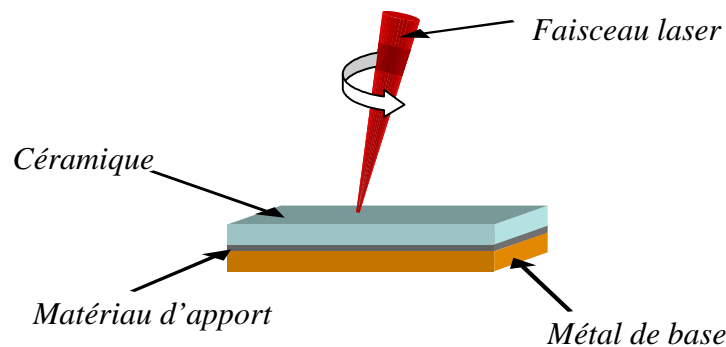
Schéma du procédé de brasage laser de l'assemblage céramique-métal
